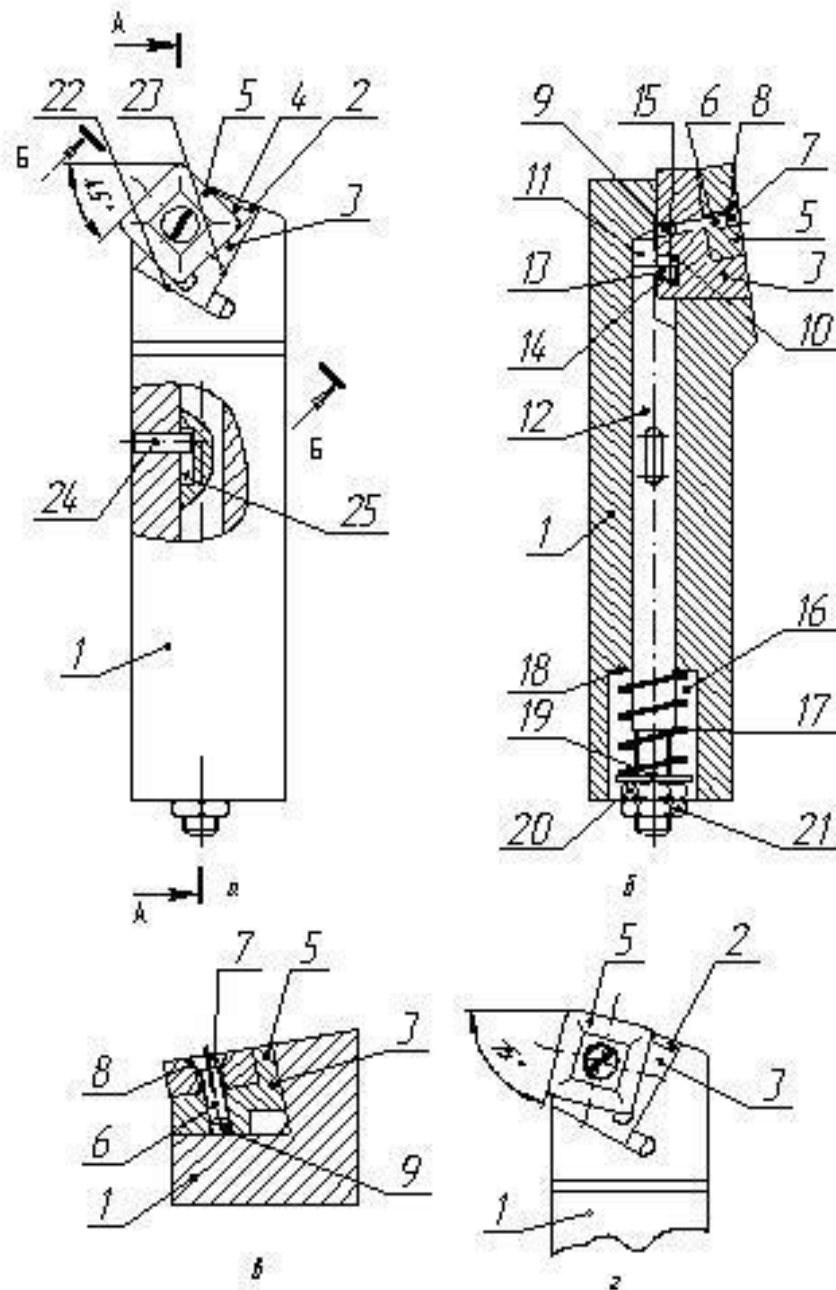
Швидкопереналагоджуваний токарний різець. а - загальний вид, б - переріз А-А, в - переріз Б-Б, г - токарний різець з кутом в плані 75[14]
